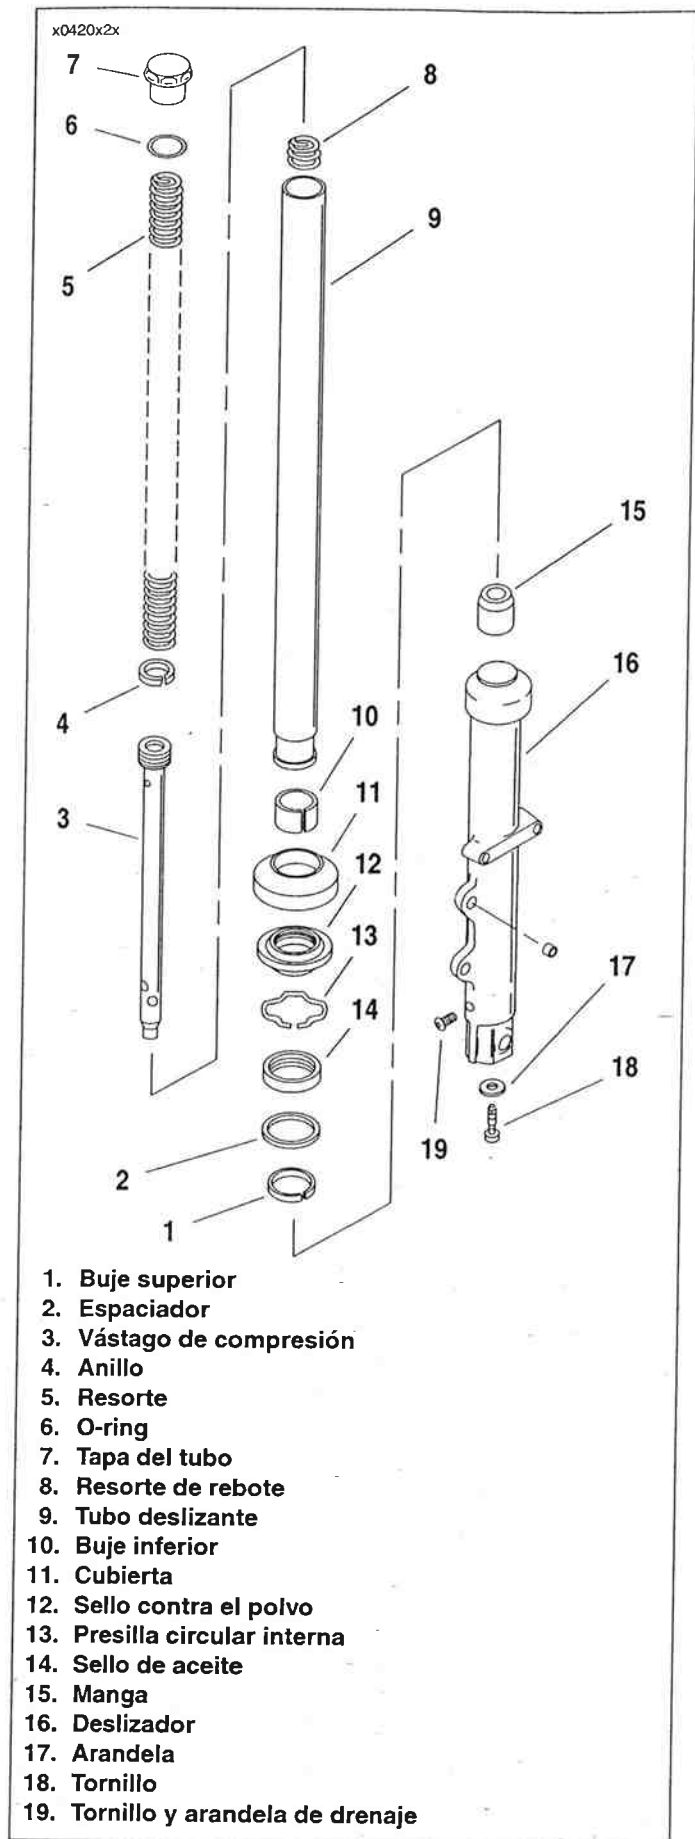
Conjunto del tubo deslizante/deslizador delantero
